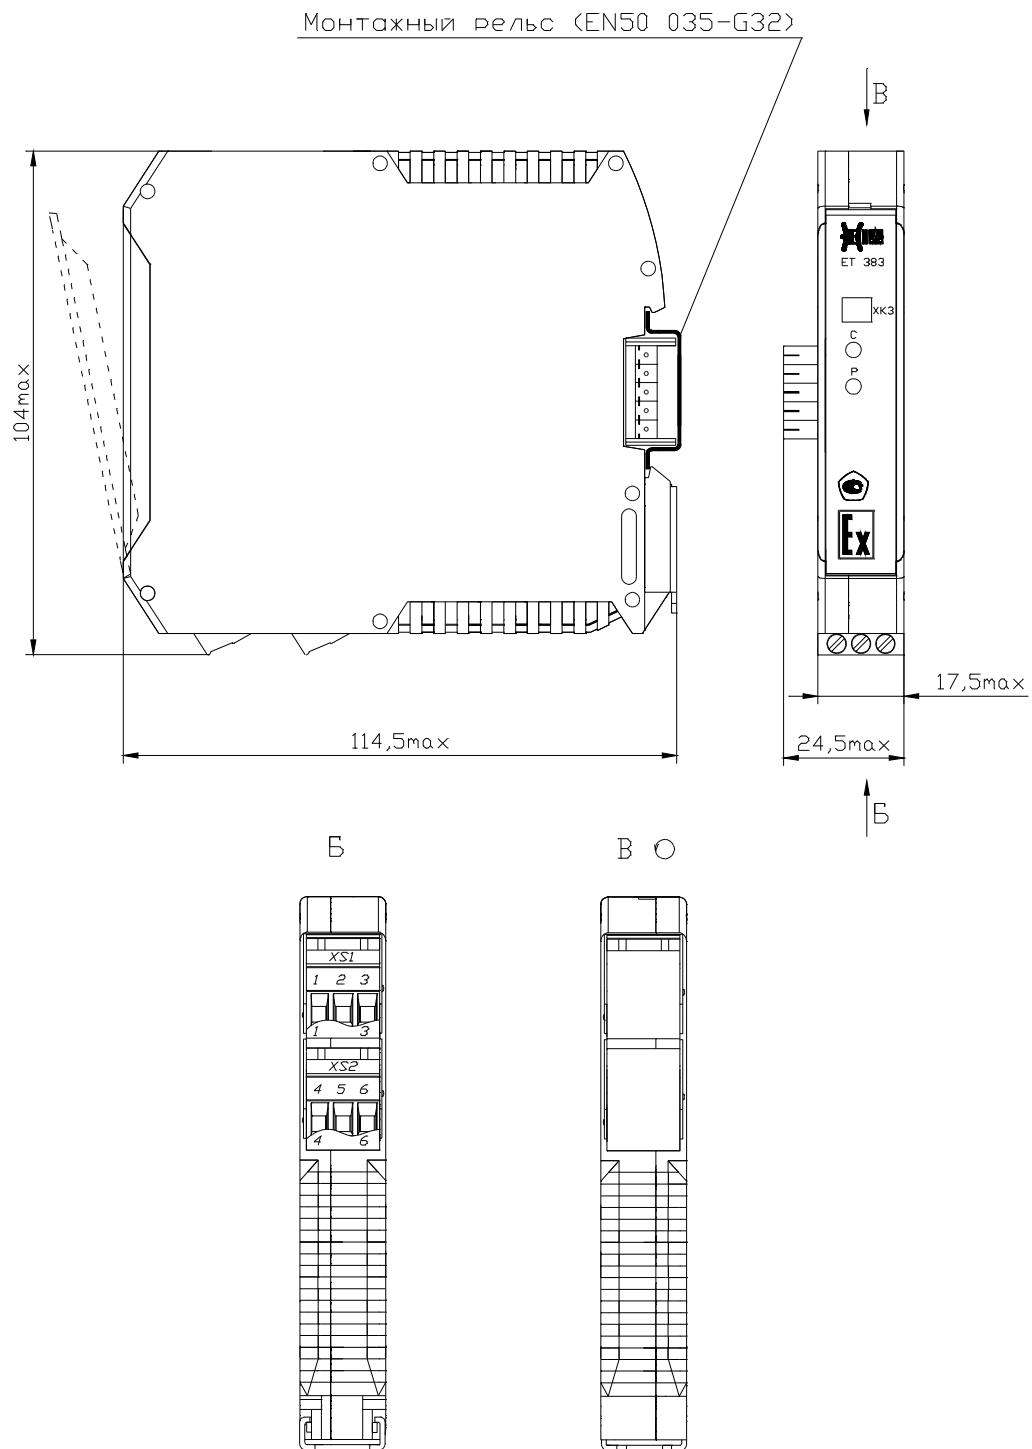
Габаритный чертеж преобразователя ET 383
